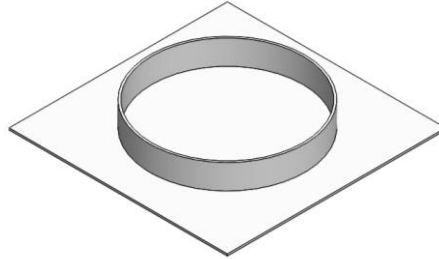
Soporte de rodamiento axial FAG 81160MB
